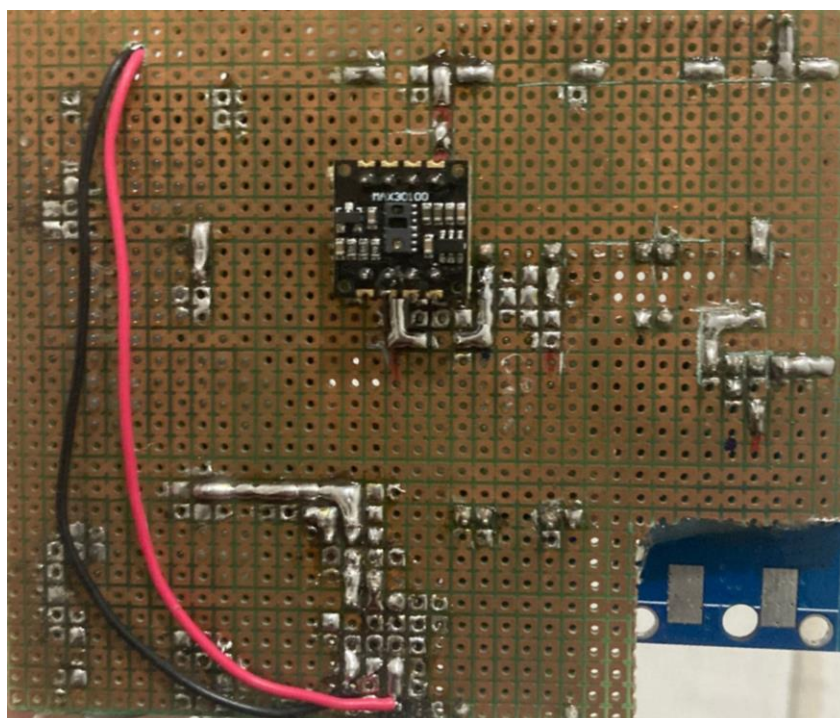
Soldagem atrás da placa fenolite com o MAX30100
